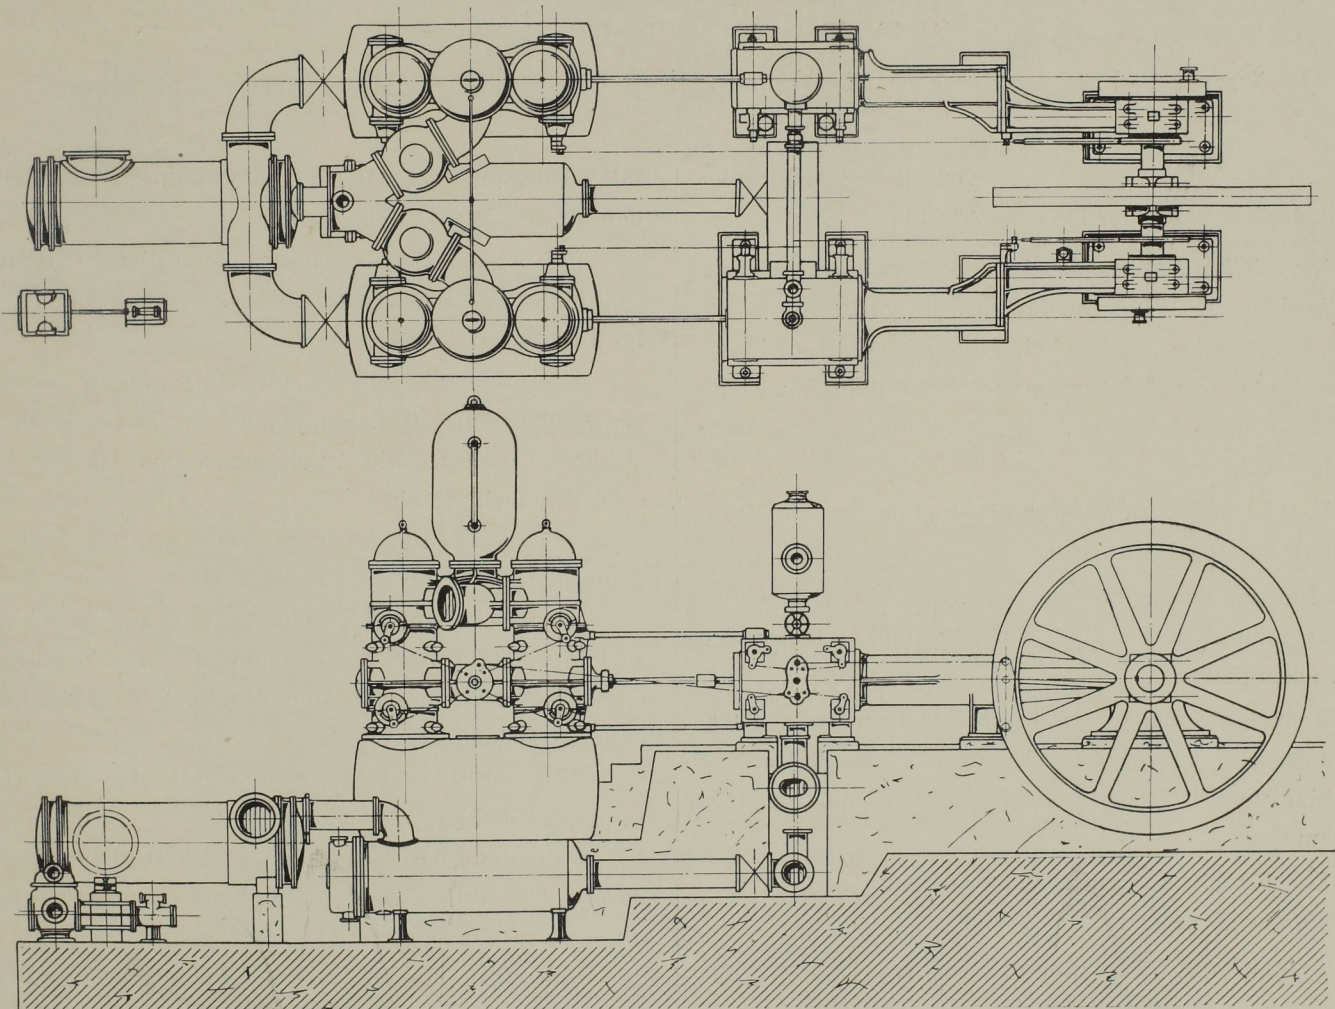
Grundriss und Seitenansicht der Pumpmaschine. Massst. 1:96.
